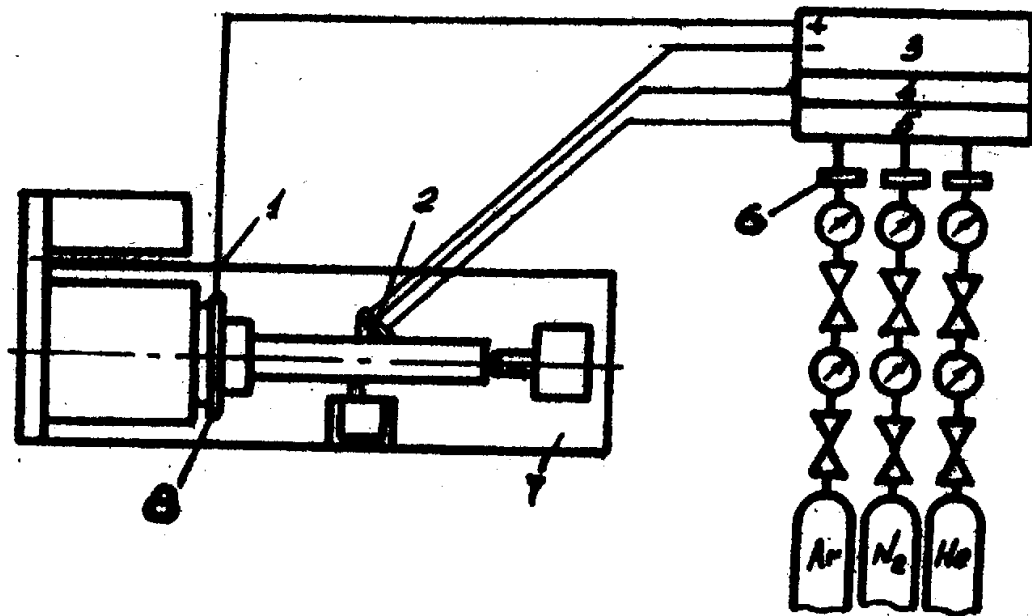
Схема установки для плазмової обробки циліндричних деталей
